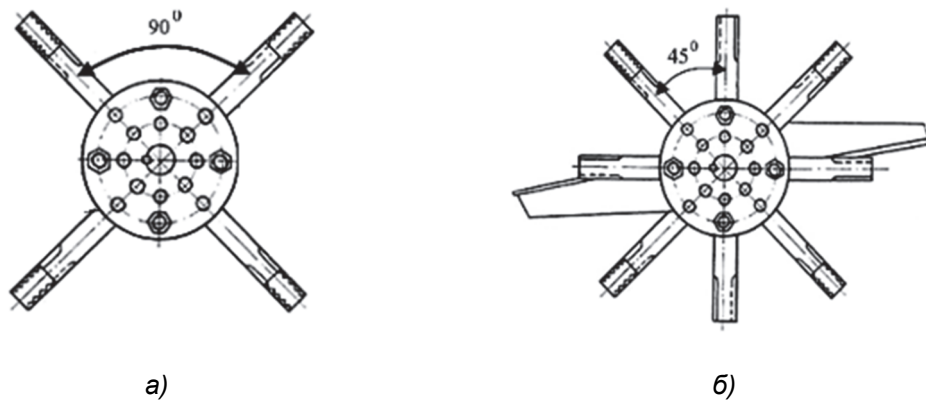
Схемы расположения ножей на роторе измельчителя-смесителя кормов ИСК-3: а — расположение смежных ножей в ярусе ротора; б — расположение ножей относительно смежных ярусов ротора
